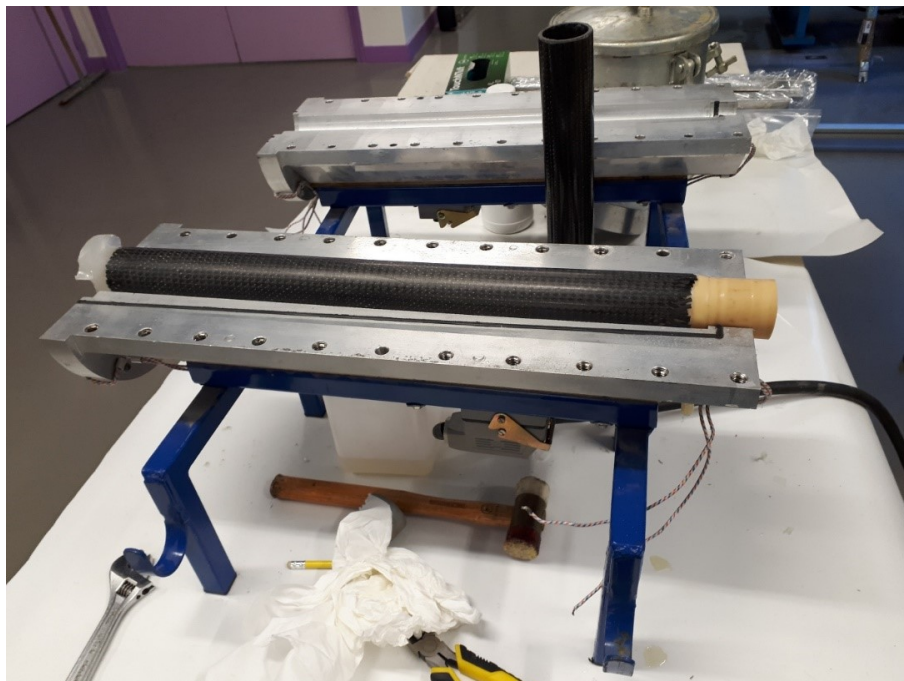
Moule ouvert avec un tube composite et sa vessie
